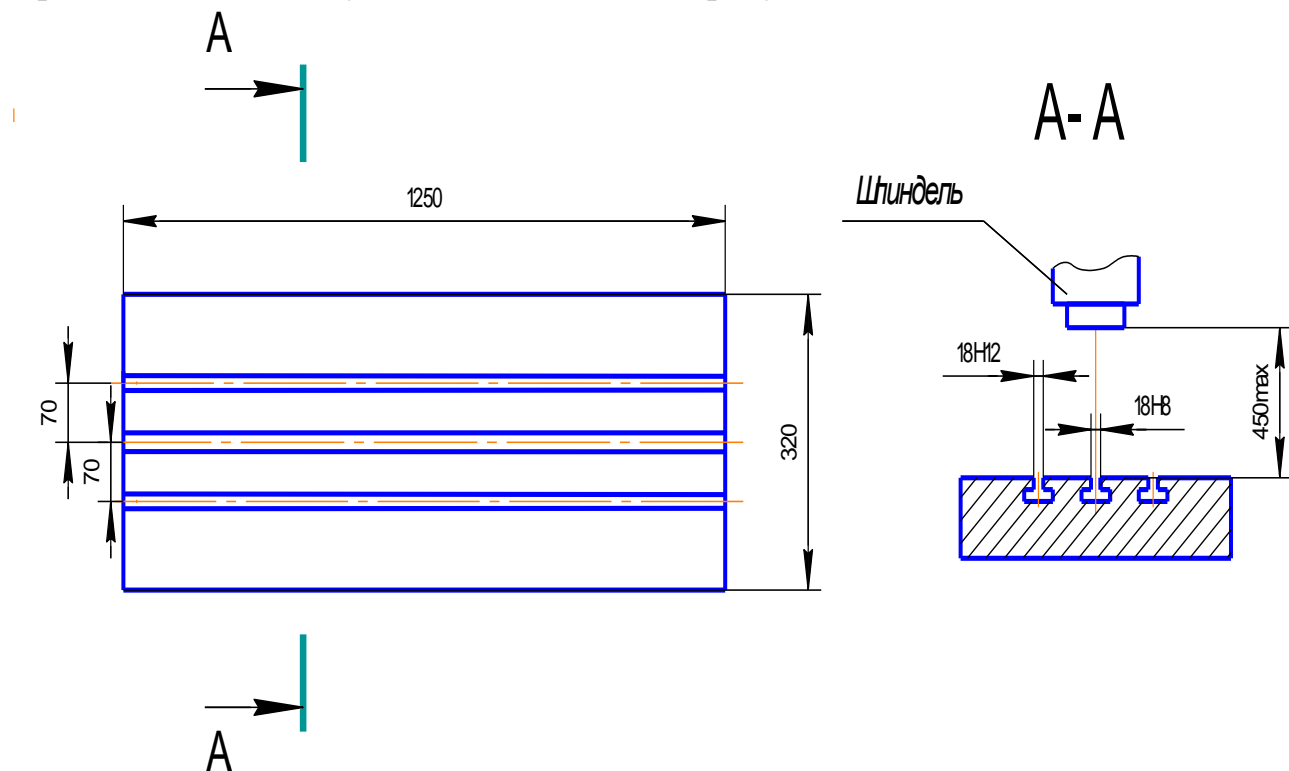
Конструкция стола станка Hekkert FU 355
